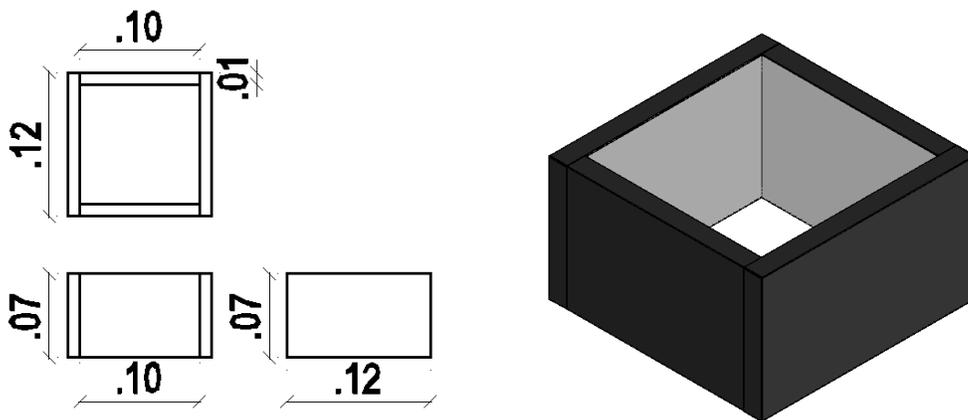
Planos molde para prototipos. Elaboración propia, creado en AutoCAD
